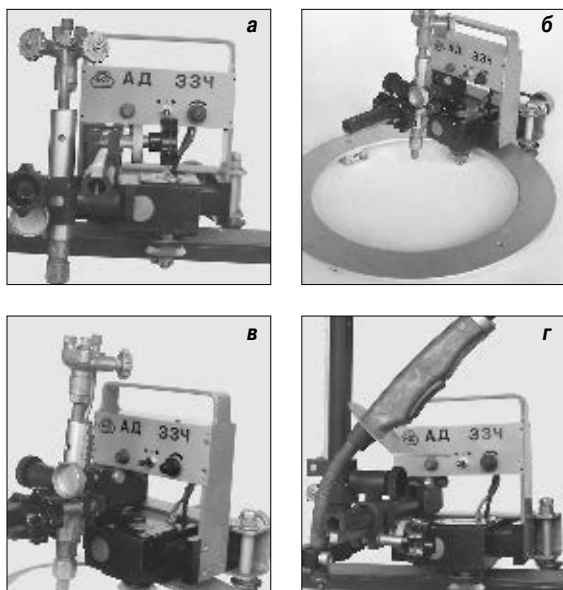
Способы применения устройства АДК-334 для газопламенной резки: а — в нижнем положении — прямой рез; б — в нижнем положении — кольцевой рез; в — в нижнем положении — криволинейный рез; г — для перемещения держателя сварочного полуавтомата
